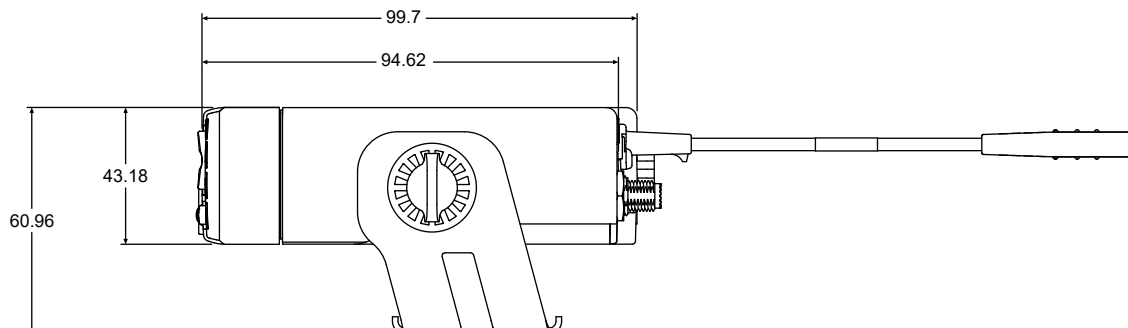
Vista lateral de montaje en el salpicadero con soporte de perfil bajo
